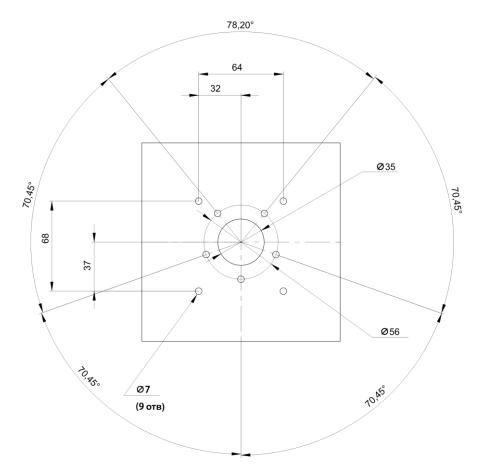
Подготовка топливного бака – крепление с помощью заклепок
